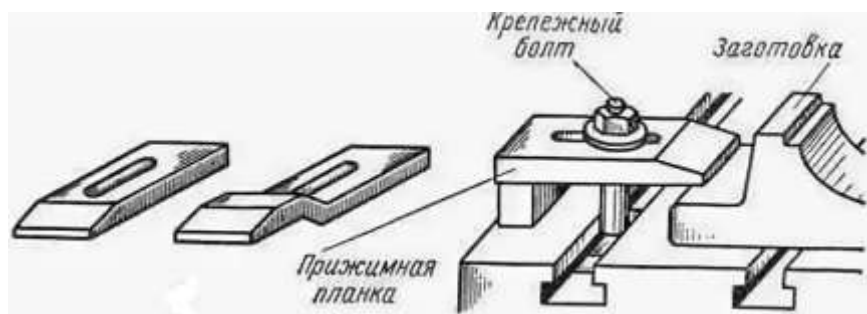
Прижимная планка и крепежный болт для закрепления
